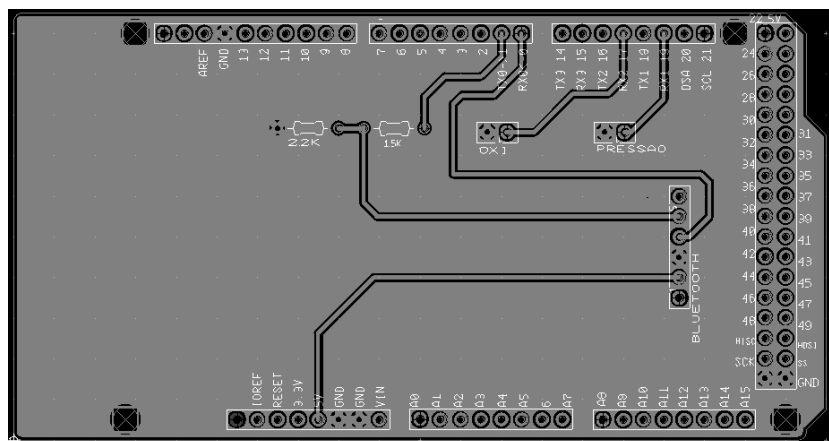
Layout da placa de circuito impresso desenvolvido com NI Ultiboard.
